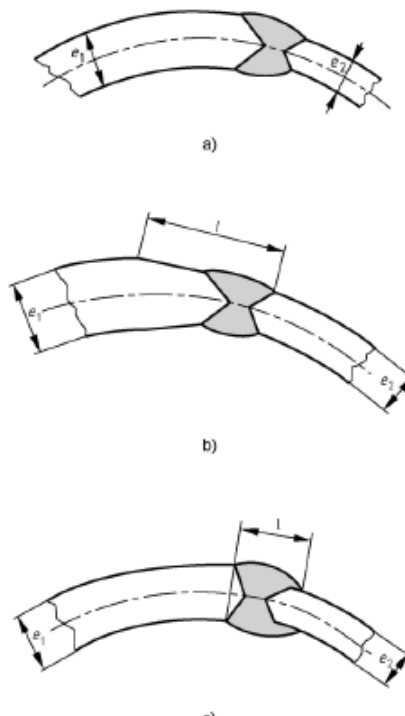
Soldadura de juntas a tope de espesor diferente
